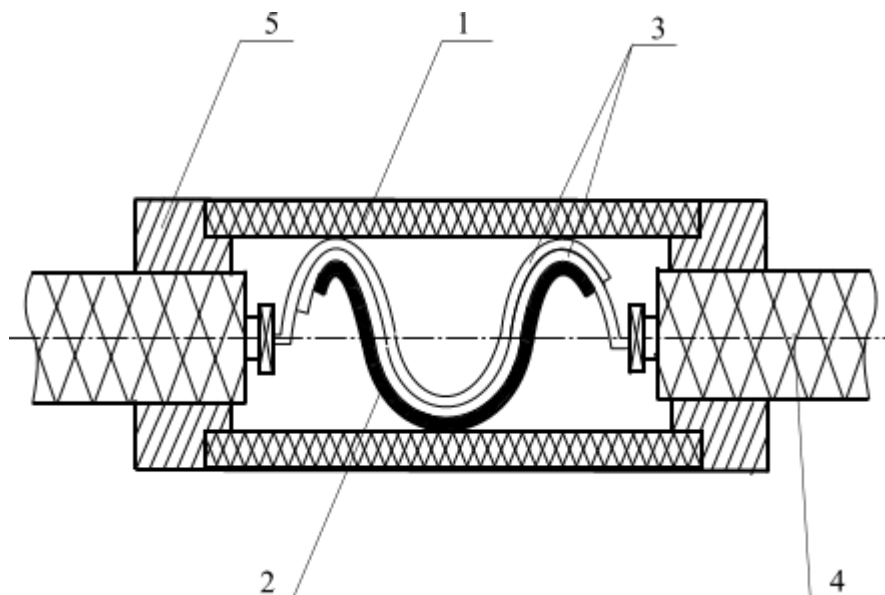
Загальний вигляд контактної вузла в розрізі:
